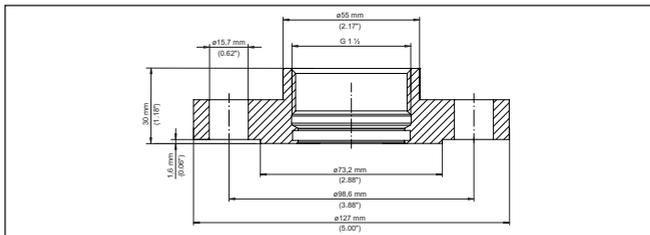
medidas adaptador de rosca G1½ (DIN 3852-X) em flange 1½" (ASME B16.5, RF) 150 lb
